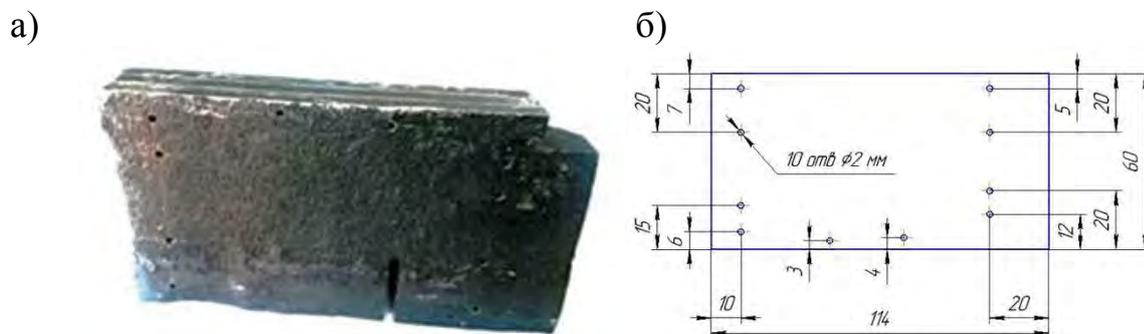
Изображение настроечного образца из фрагмента боковой рамы (а); чертеж настроечного образца (б)
